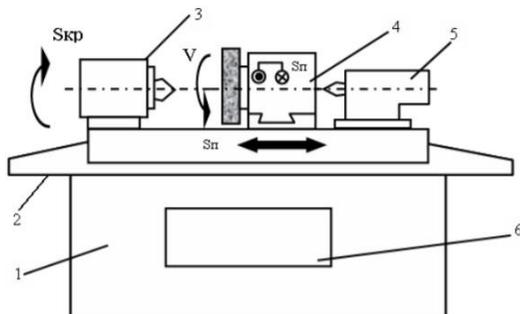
Общий вид кругло-шлифовального станка
